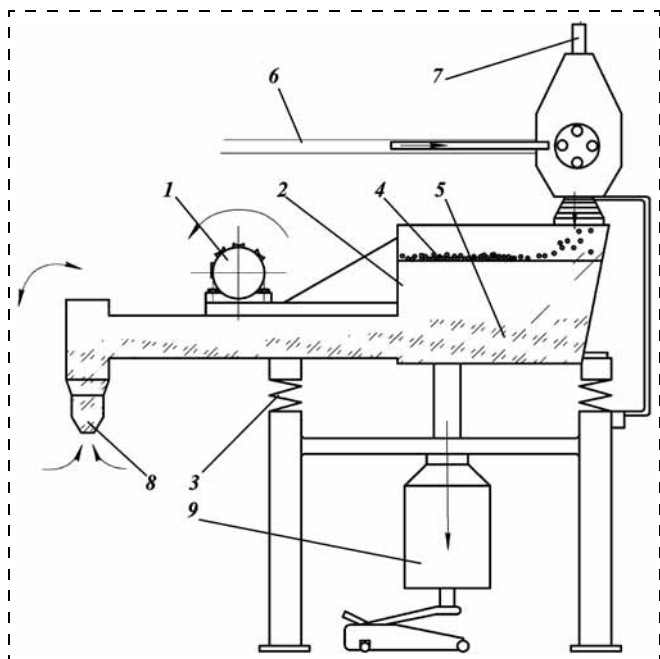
Конструктивная схема вибросепаратора с дробилкой:
